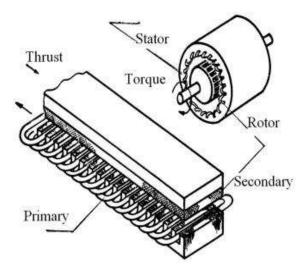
Motor rotacional y motor lineal. Tomado de [8]
